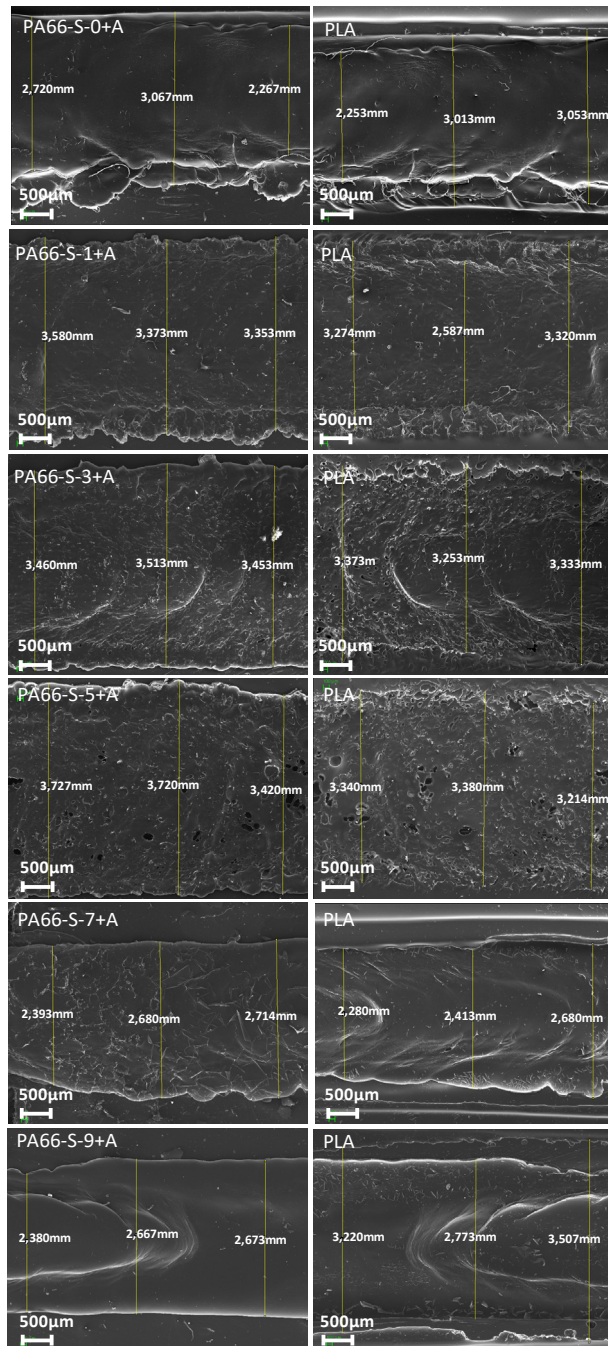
Determinación del cordón de soldadura de las soldaduras en los sistemas PLA/PA66 ensayados a resistencia a la cizalladura.
